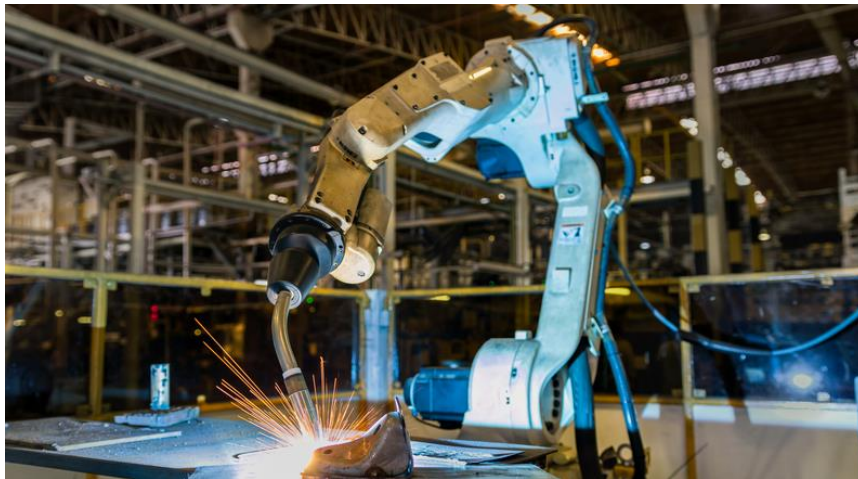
Esempio di manipolatore dotato di tool per la saldatura come end effector
